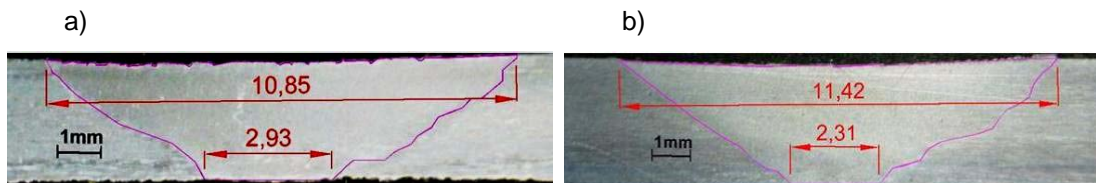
Macrografías de probetas soldadas T con pin cónico: a) 1Co-T; b) 2Co-T.
